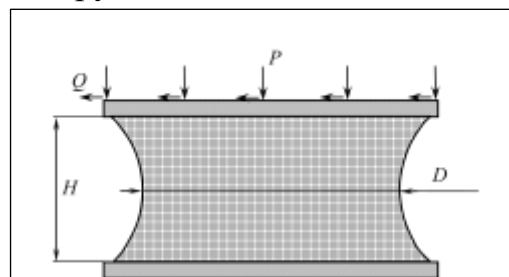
Виброакустический резиновый изолятор с композитными вставками
